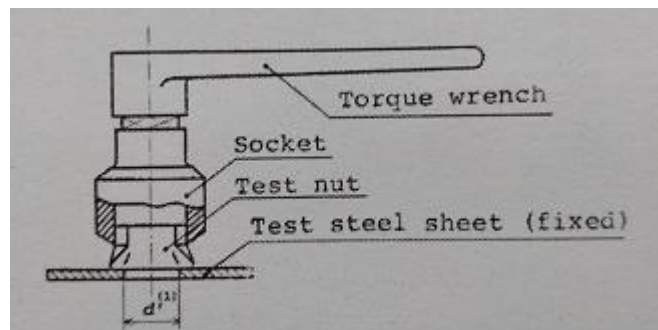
Muestra esquemática de ensayo por torsión de tuerca soldada por proyección.
